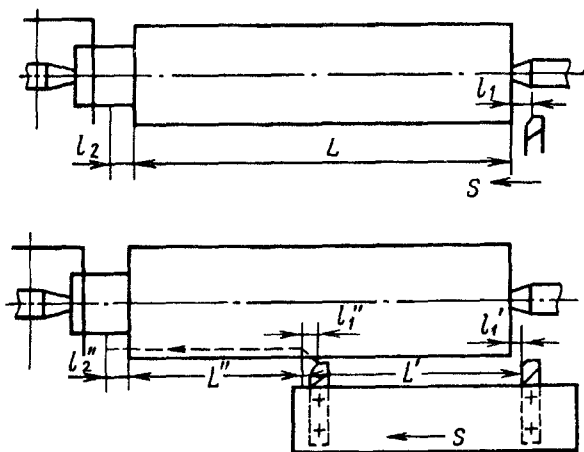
Схемы обработки одной поверхности детали одним и двумя резцами
